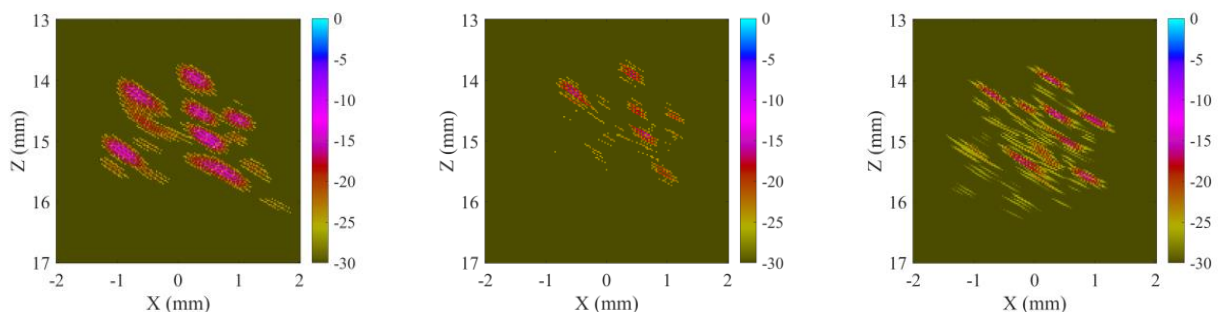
Reconstructions du cas mixte en ondes T (quadrant 1).
